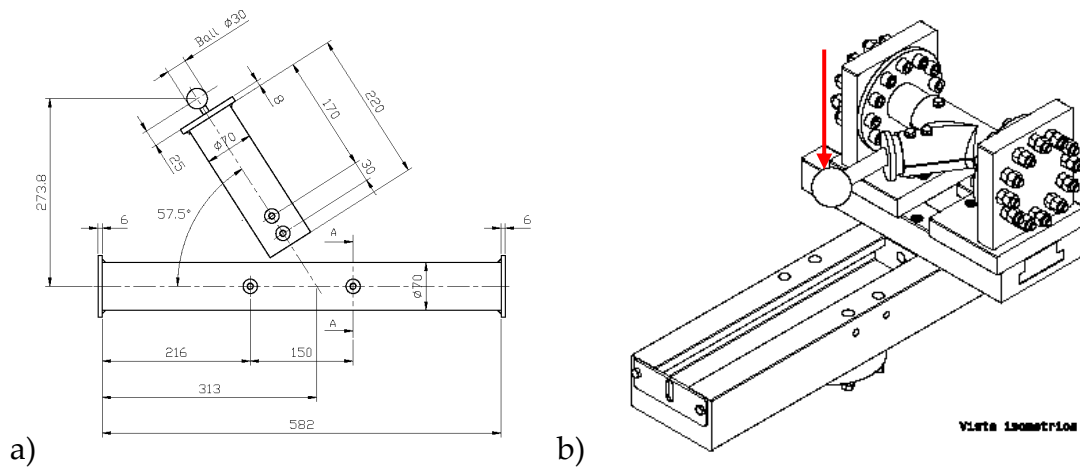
Aparejo de prueba. a) croquis inicial, b) diseño final
